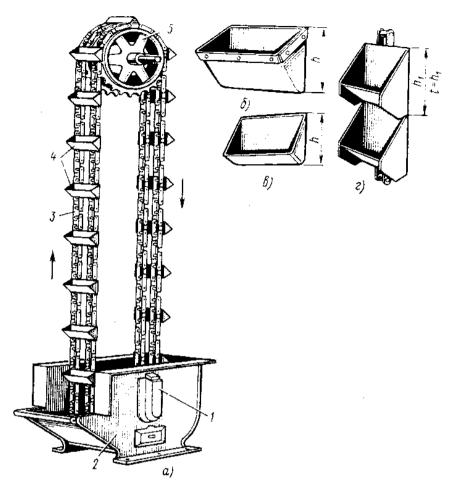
Ковшовый конвейер (элеватор): а — общий вид; б — глубокий ковш; в — мелкий ковш; г — чешуйчатый (остроугольный) ковш; 1 — натяжное устройство; 2 — корпус; 3 — лента или цепь конвейера; 4 — ковши; 5 — приводное устройство
